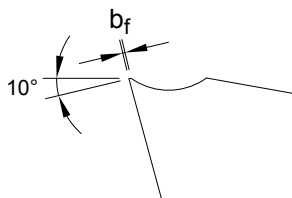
Neutrale openingshoek voor afwerking en voorbereiding
